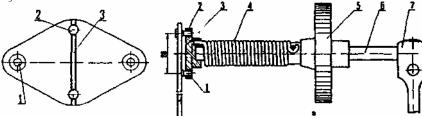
Передняя втулка вала пускового механизма: 1 - отверстие для крепления втулки, 2 - глухие отверстия для кольцевого ключа; 3 - паз для отвертки
